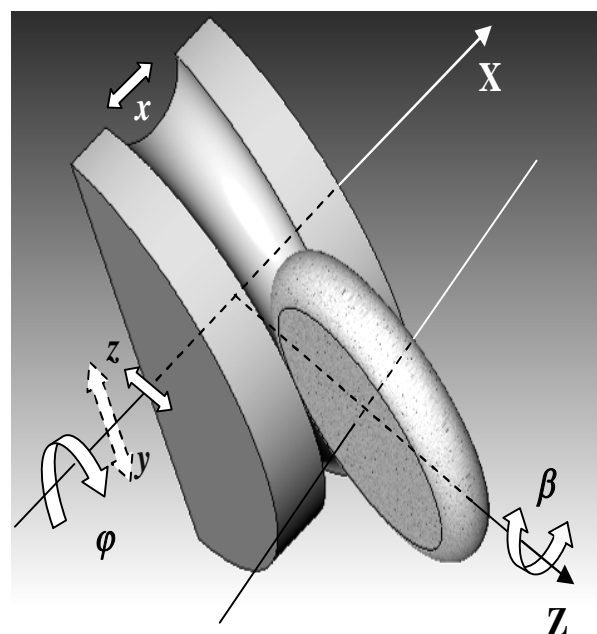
Схема формообразования профиля калибра на станке с ЧПУ
